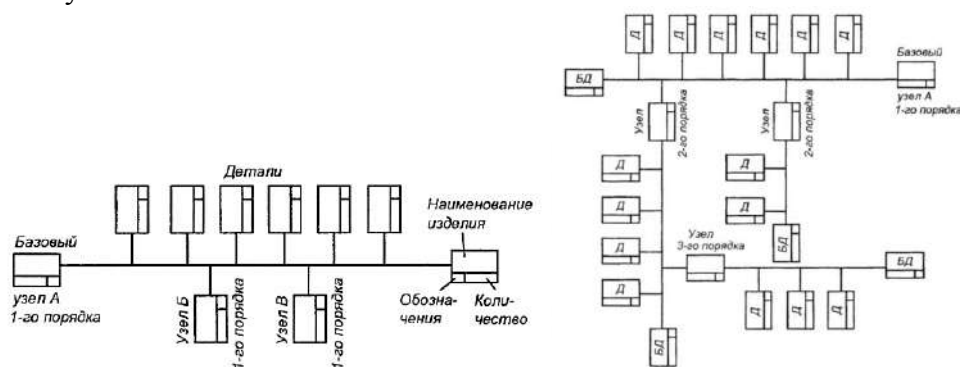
Схема общей сборки изделия Рис. 32. Схема узловой сборки: БД — базовая деталь; Д — деталь
